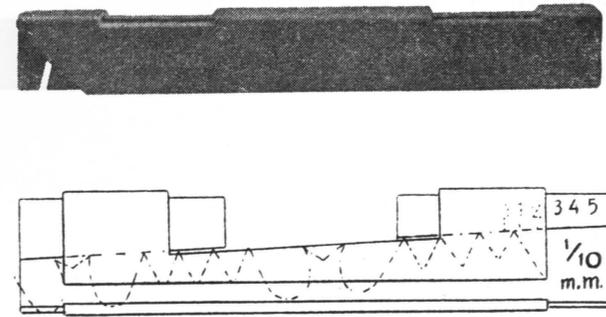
Abrichtgerät für Hobelbezeichnung der Spannsägen.
